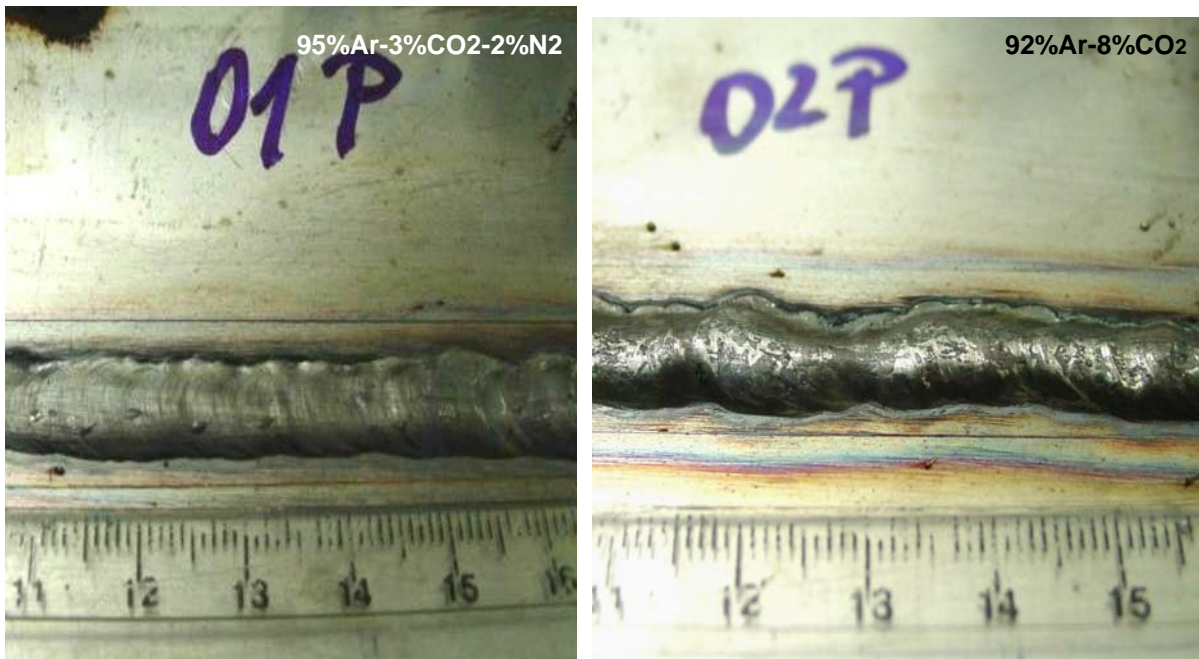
Cordão de solda - MAG-P com comprimento do eletrodo de 10 mm
